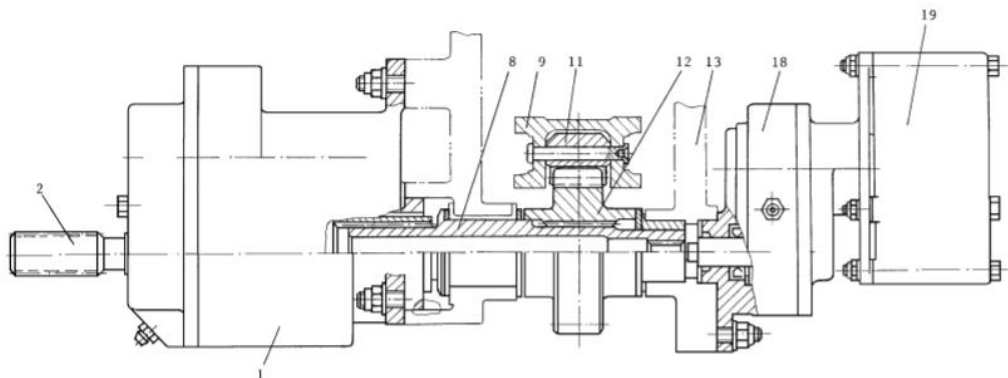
Механізм переміщення передкрилків № 5. 1- приводний редуктор; 2- вал-шестерня; 3- кришка; 4- корпус; 5- шестеренчатий вал; 6- шестерня; 7- ліва щоча каретки; 8- вал ведучої шестерні; 9- рейка переміщення; 10- валик; 11- зубчатий сектор; 12- ведуча шестерня; 13- права щоча каретки; 14- підшипник.
